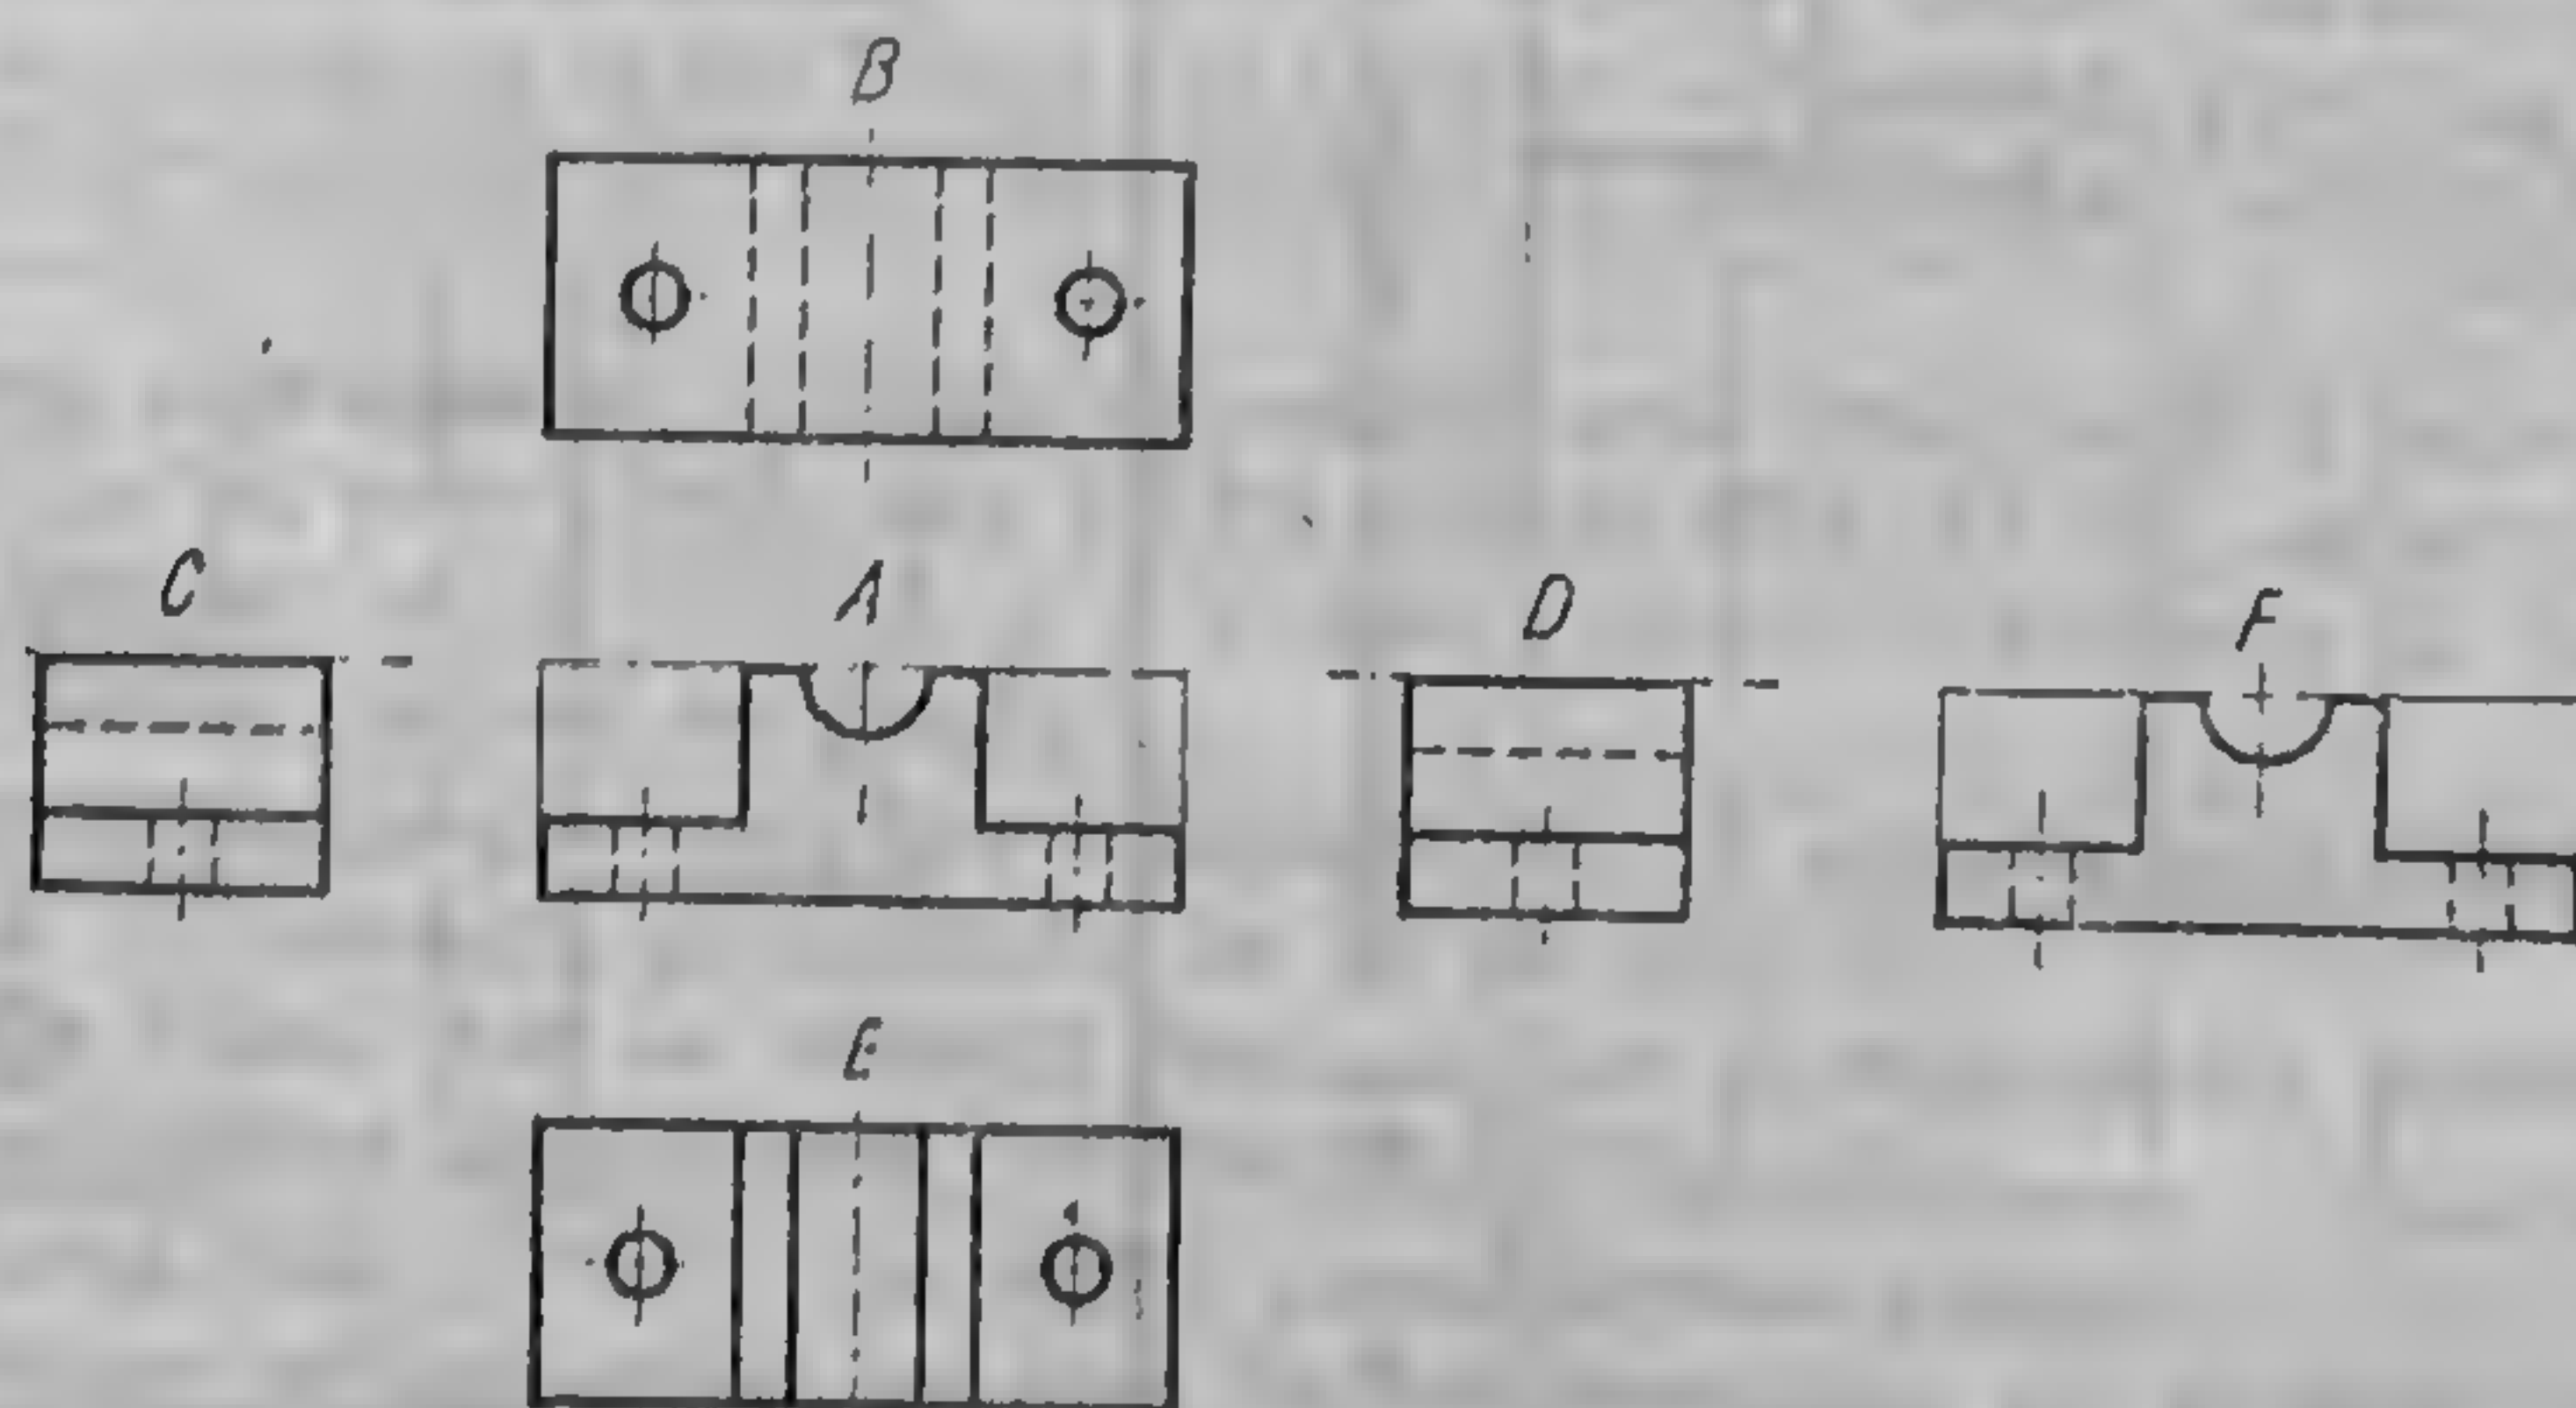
Dispunerea în plan a dreptunghiurilor minime de încadrare și a proiecțiilor.
